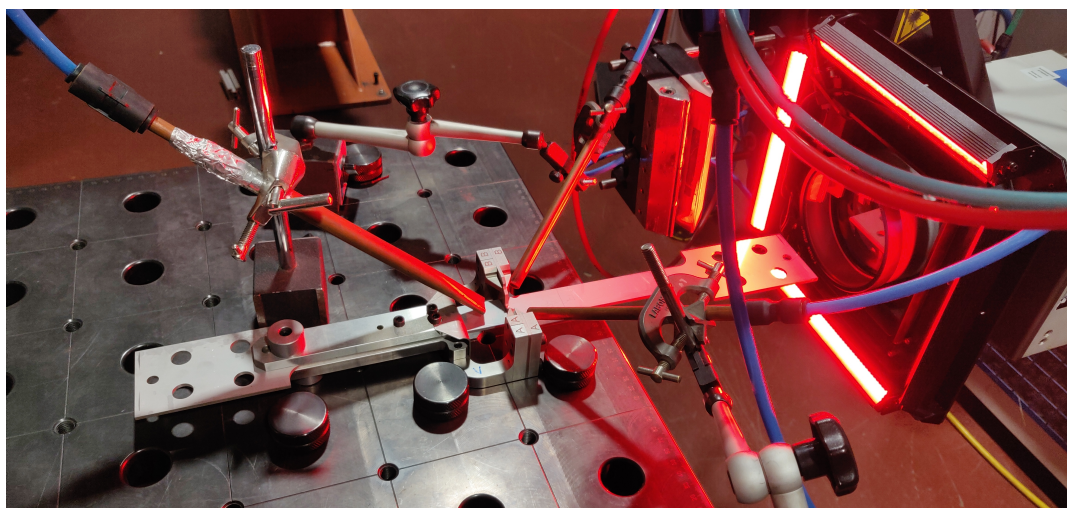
Vue globale de la mise en place pour le soudage des aubes.
